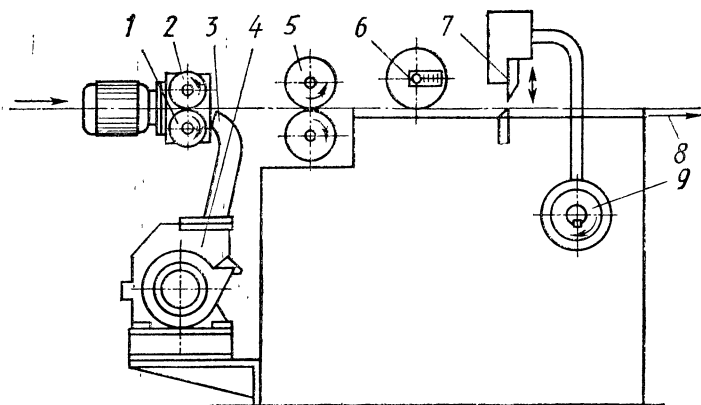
Устройство для обрезки кромок, замера метража и поперечной резки линолеума:
